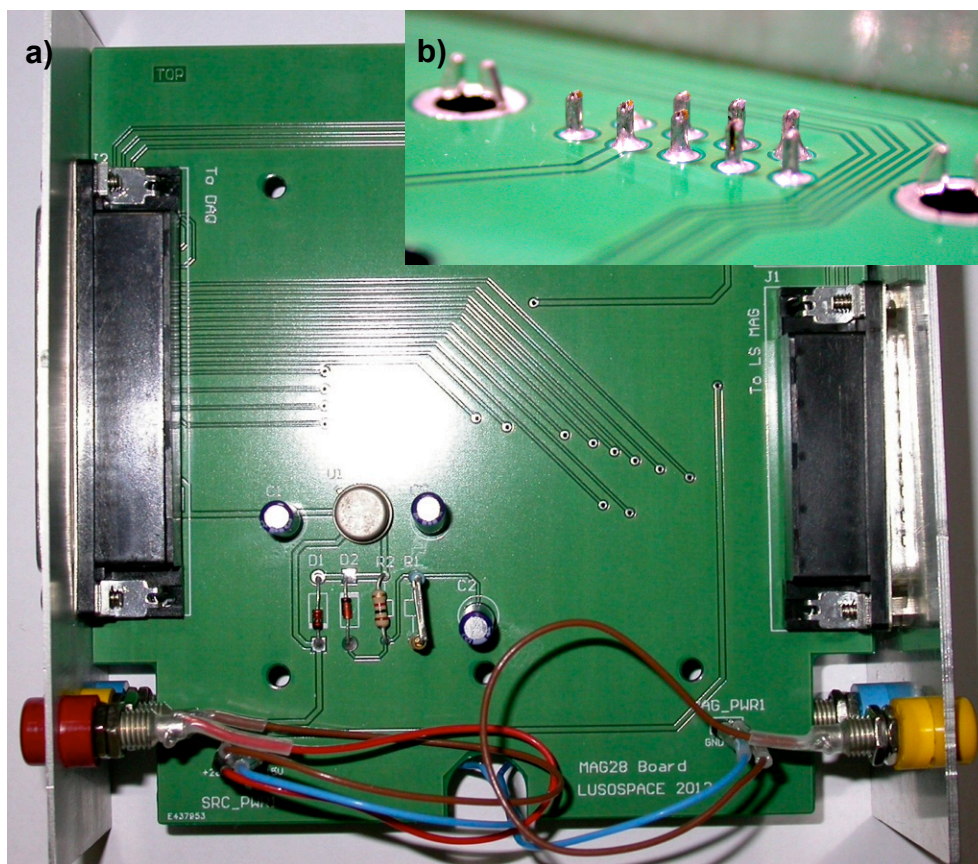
Camada a) Top b) Bottom da PCB.
